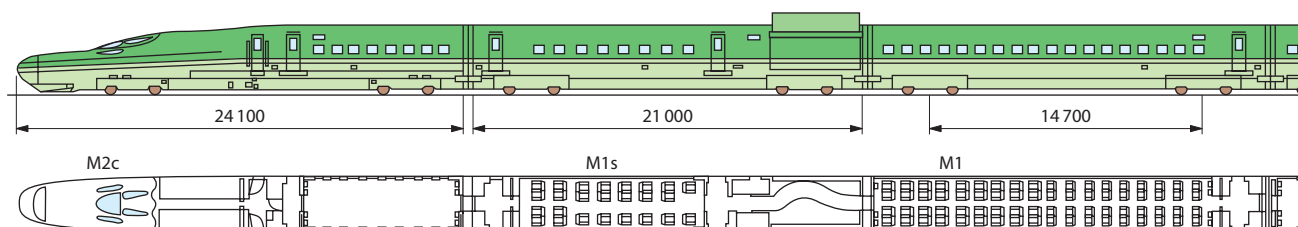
Схема и основные размеры половины состава поезда Fastech 360 Z
